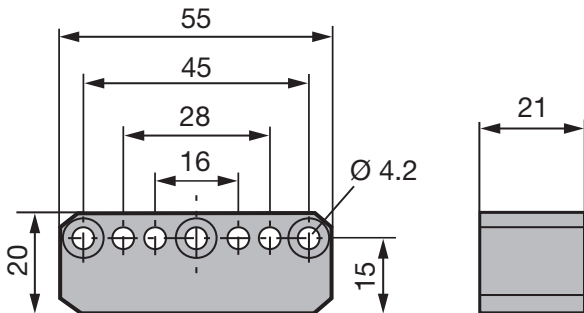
Dimensions de montage du capteur de position BTL5-P-5500-2
